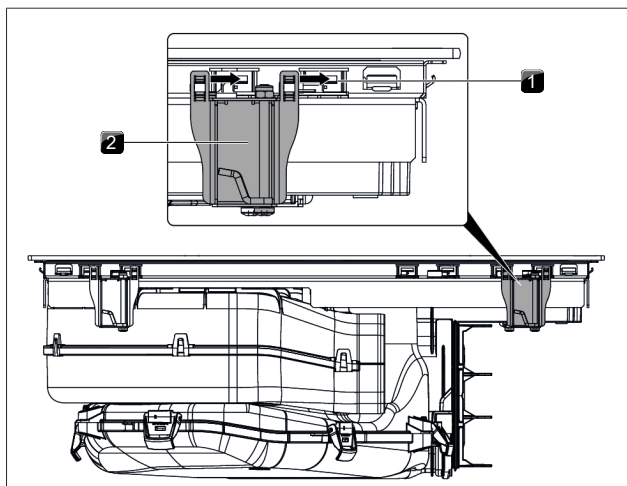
Tesniaca páska pri zapustenej montáži
